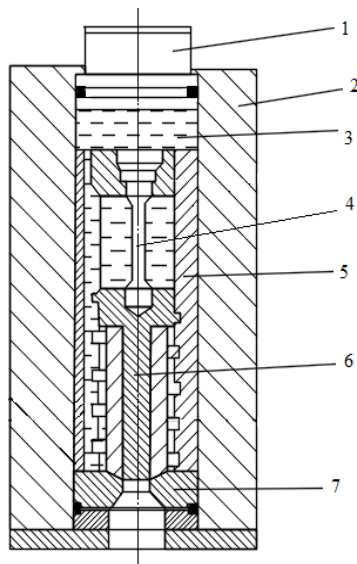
Наладка пластометра для испытания образцов на кручение (а.с. 1105780). 1 – пуансон; 2 – герметичный контейнер; 3 – рабочая среда; 4 – испытуемый образец; 5 – стакан; 6 – вспомогательный образец; 7 – матрица
